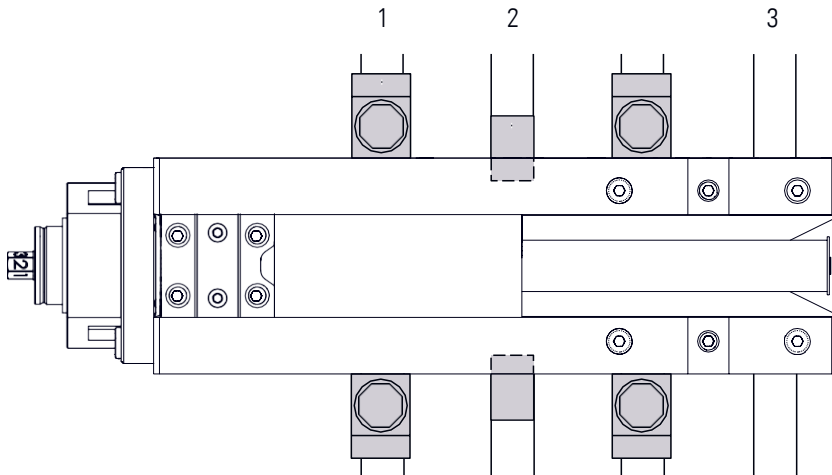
Montage auf einem Maschinentisch (Beispielbild mit NC8 -125 M)
